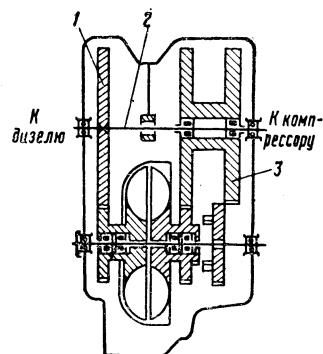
Схема привода компрессора непосредственно от коленчатого вала дизеля, минуя гидромуфту:
